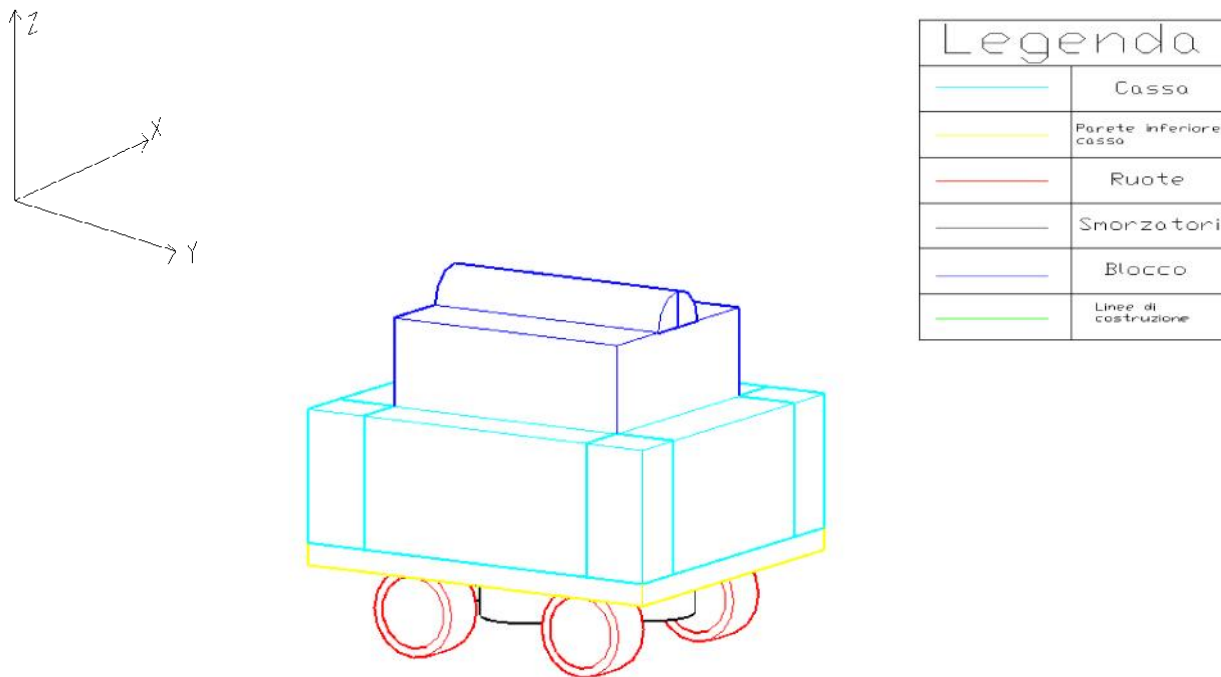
27 Vista prospettica del carrello con i suoi elementi fondamentali e con il blocco all'interno
